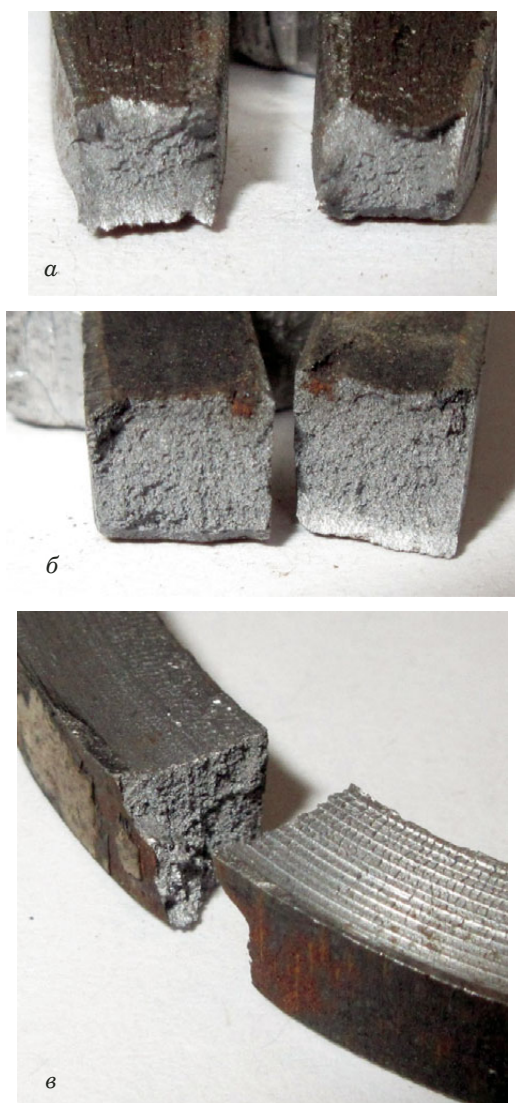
Виды изломов образца № 1: *a* — продольный образец трубы вблизи разрыва; *b* — продольный образец трубы с противоположной разрушению стороны; *в* — кольцевой образец трубы
